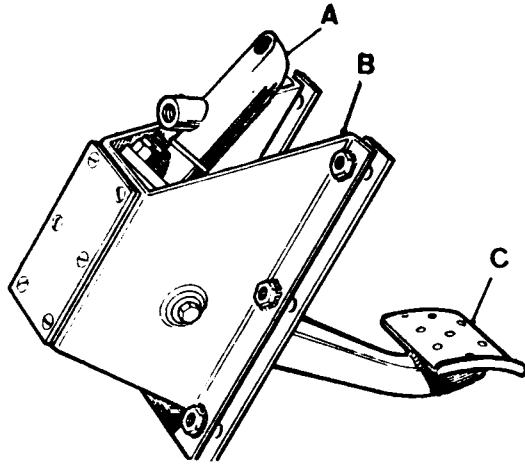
Conjunto del soporte, pedal y cilindro principal.
